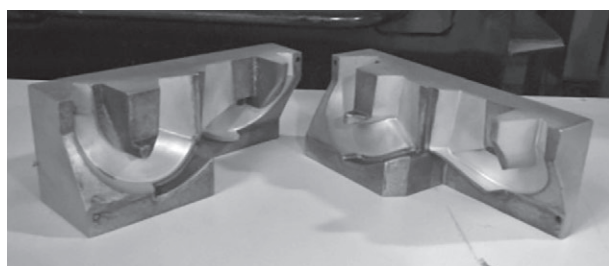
Стержевая оснастка для производства отливки «Колесо насосное»
